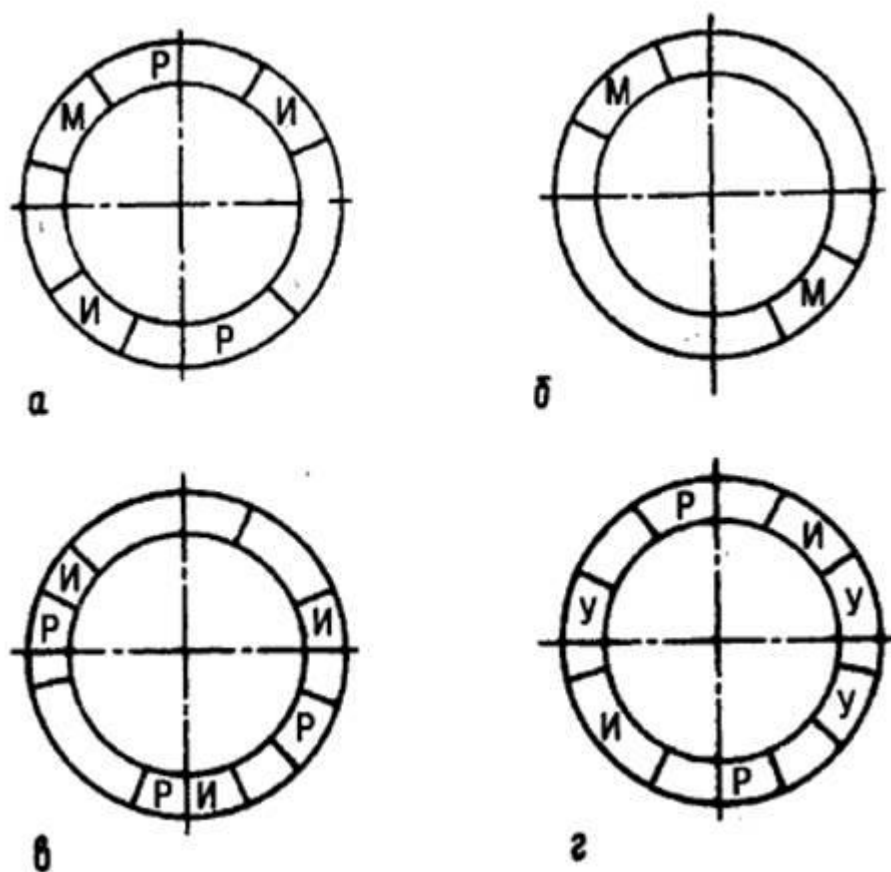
Схемы вырезки образцов из вертикальных стыков:
